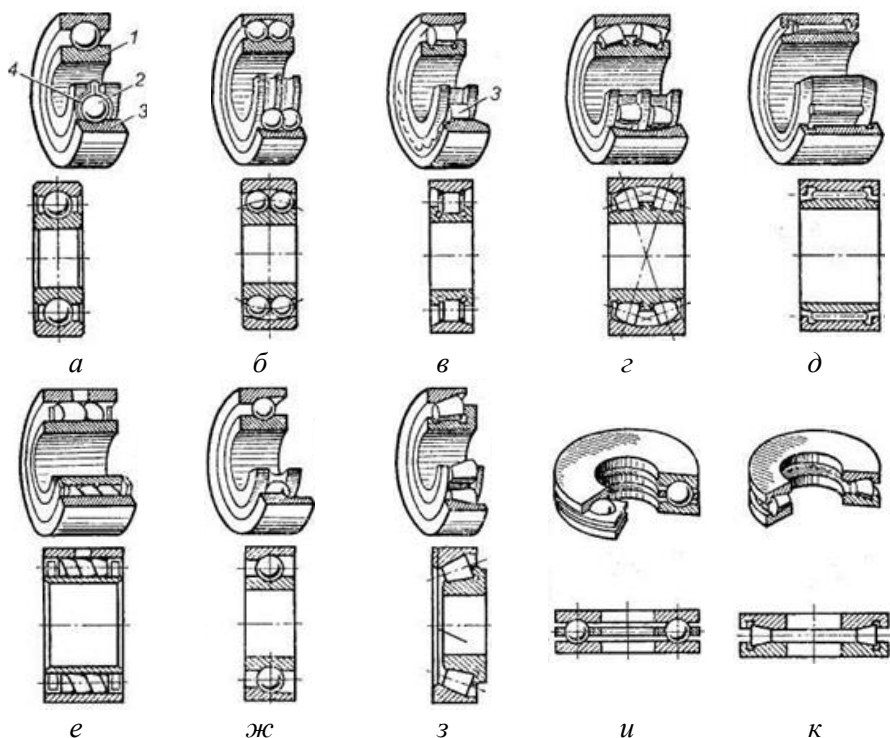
Подшипники качения: а, б, в, г, д, е – радиальные подшипники; ж, з – радиально-упорные подшипники; и, к – упорные подшипники; 1 – внутреннее кольцо; 2 – тело качения; 3 – наружное кольцо; 4 – сепаратор
